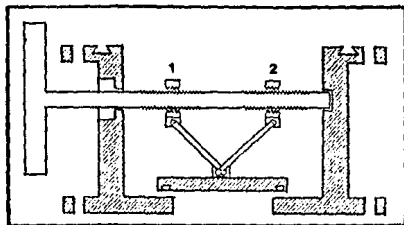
VALVULA BAFLE. (1) CUERDA IZQUIERDA, (2) CUERDA DERECHA.
